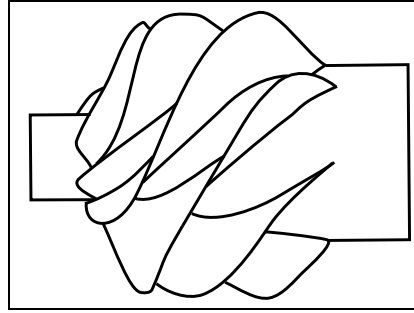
Rotor de la pompe axiale ; exemple 3.5
